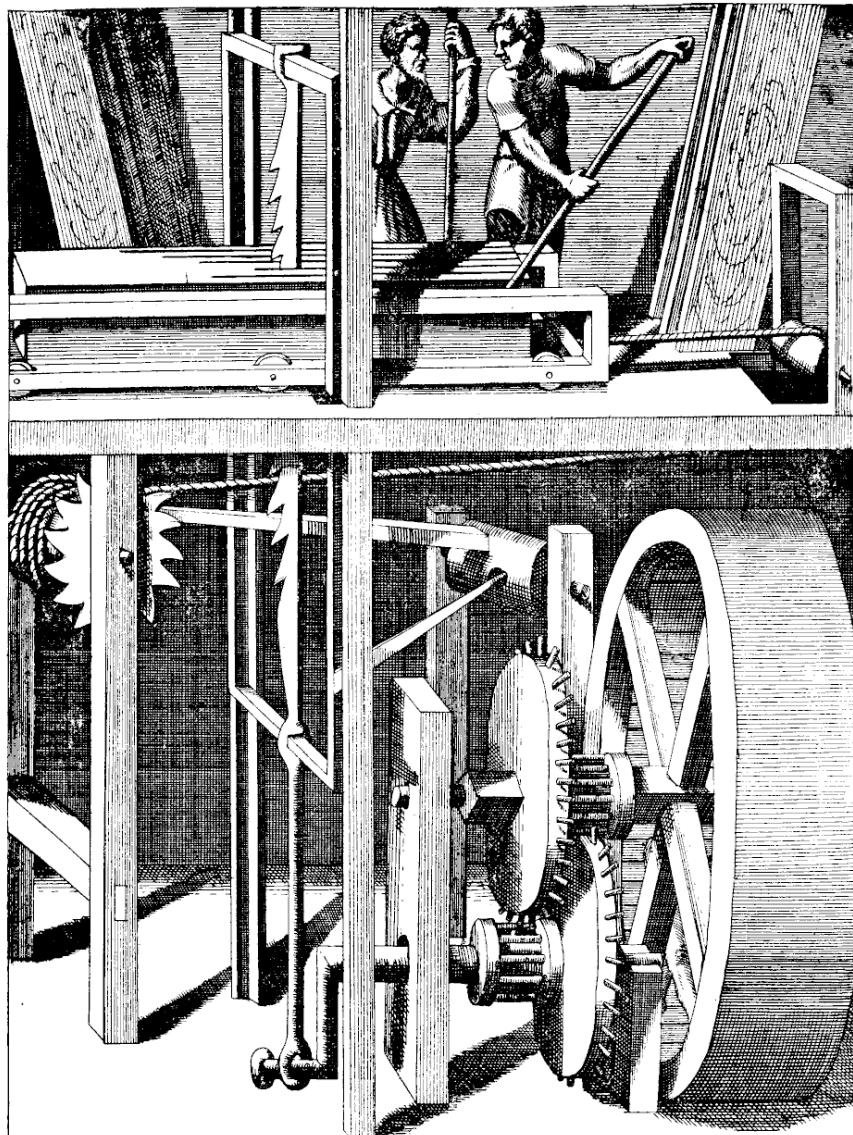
Machine à scier le bois au XVII^e siècle (STRADA).
